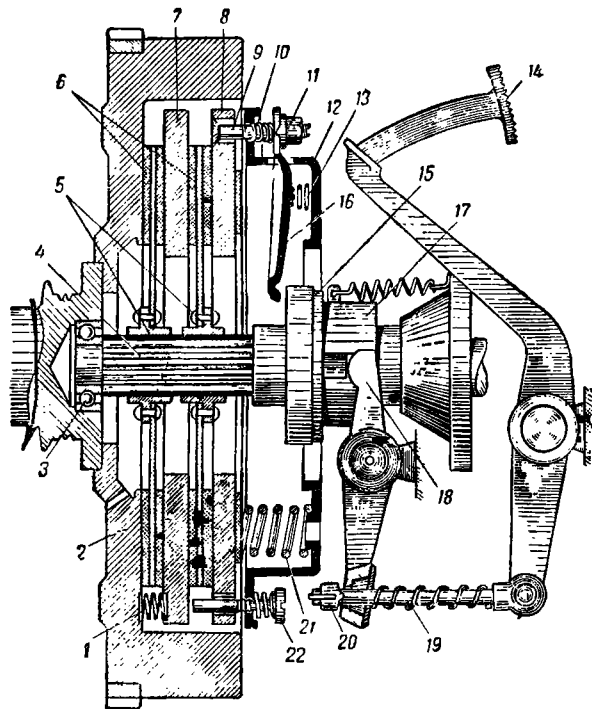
Схема и детали двухдискового сцепления (автомобиль ЗИЛ-150).
